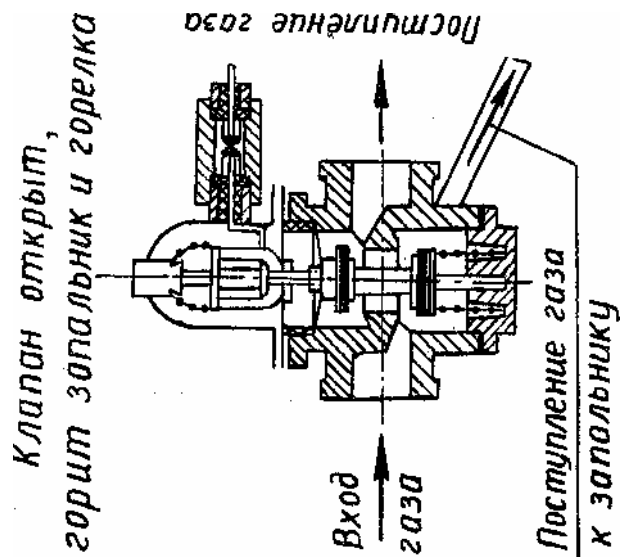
Схема магнитного газового клапана: 1 – провода; 2,6 – тарелки клапана; 3,4 – клапаны; 5 – пружина; 7 – шток; 8 – корпус; 9 – мембрана; 10 – колпак; 11 – сердечник; 12 – якорь.
